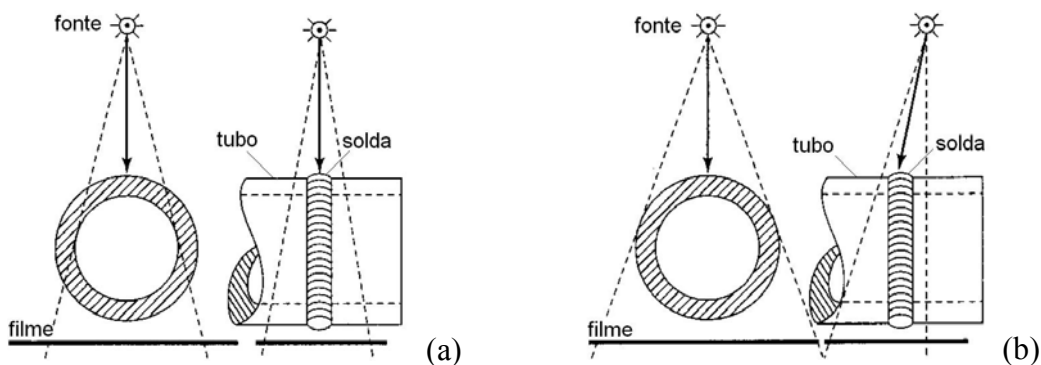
Configurações do ensaio radiográfico de juntas soldadas com exposição do tipo PD-VD para técnicas com a fonte em posição (a) alinhada ou (b) inclinada em relação ao plano longitudinal da solda (ASME, 2004).
